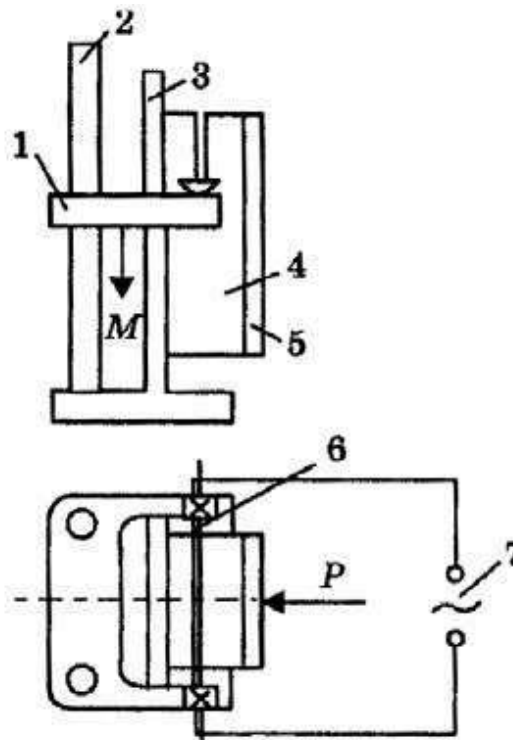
Схема термоэлектрического метода резки пенопласта: 1 - траверса; 2 - стойка; 3 - упор; 4 - заготовка; 5 - прижим; 6 - высокоомная проволока; 7 – источник
